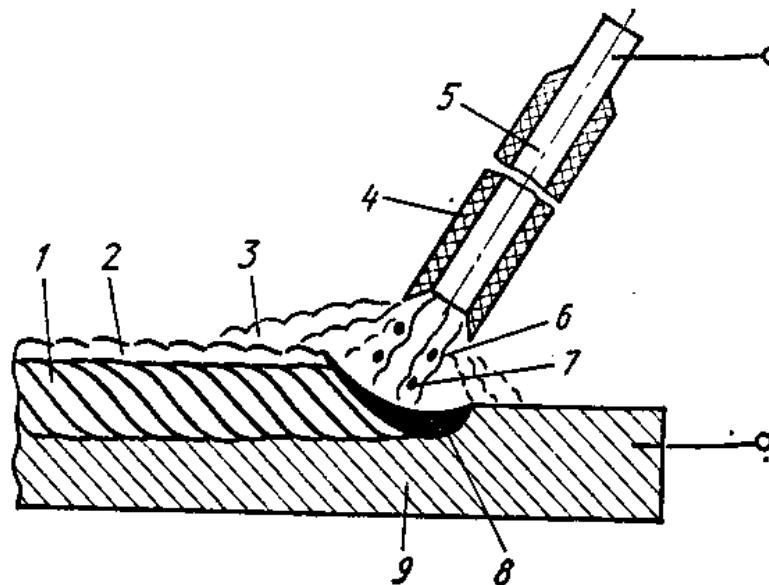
Схема ручного дугового зварювання металевим покритим електродом:
